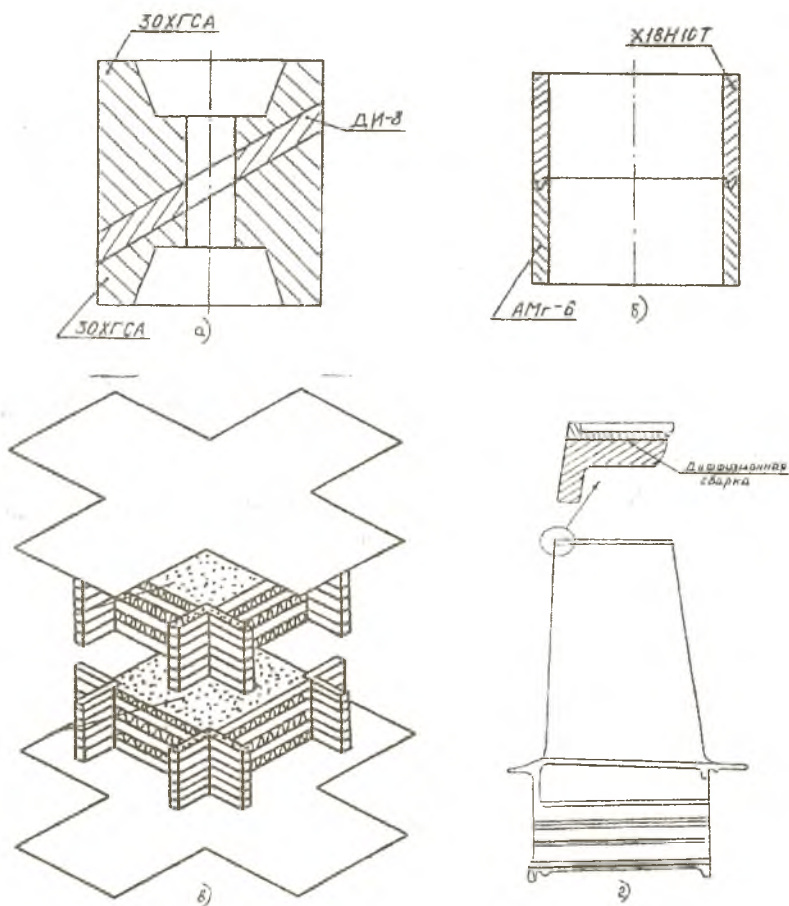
Детали и узлы авиационных ГТД, изготавливаемые с помощью диффузионной сварки (а, г) и термовакuumной клиновой сварки (б) и пайки (в): а - ротор турбогенератора, б - биметаллический трубчатый переходник, в – блок пластинчатого теплообменника; г – консольная турбинная лопатка
